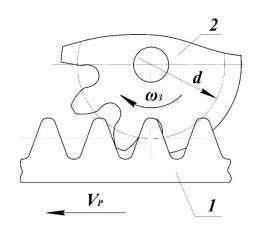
Нарезание колеса инструментальной рейкой:
